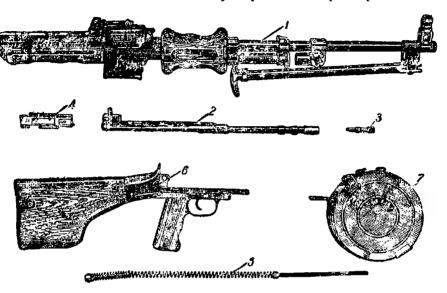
Основные части и механизмы ручного пулемета: I— ствол со ствольной коробкой, прицельным приспособлением и сошкой; 2— затворная рама с газовым поршнем; 3— рукоятка перезаряжания; 4— затвор; 5— возвратный механизм; 6— спусковая рама с прикладом и спусковым механизмом; 7— коробка с лентой
